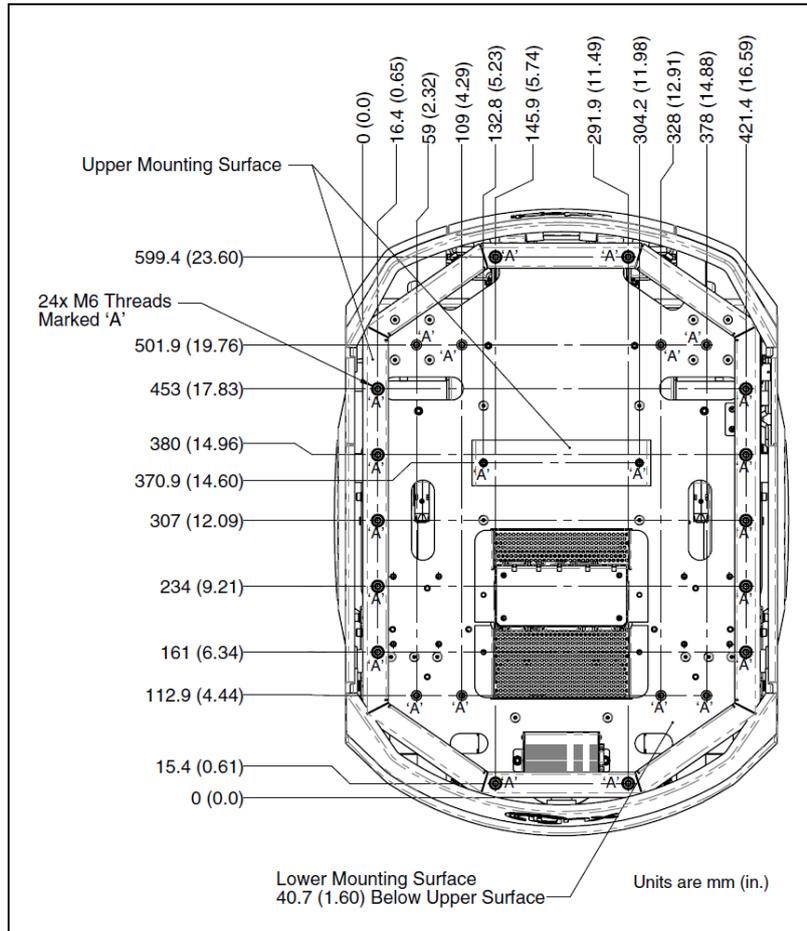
Abmessungen des Plattformdecks zur Befestigung einer Nutzlaststruktur mit M6-Gewindeschrauben
